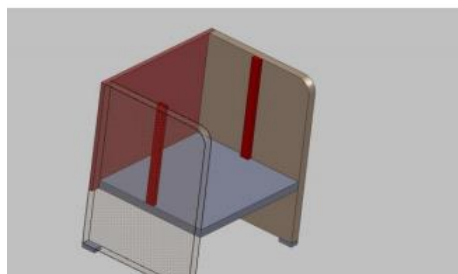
(Estrutura externa de apoio do conjunto por Wilton Alano)
